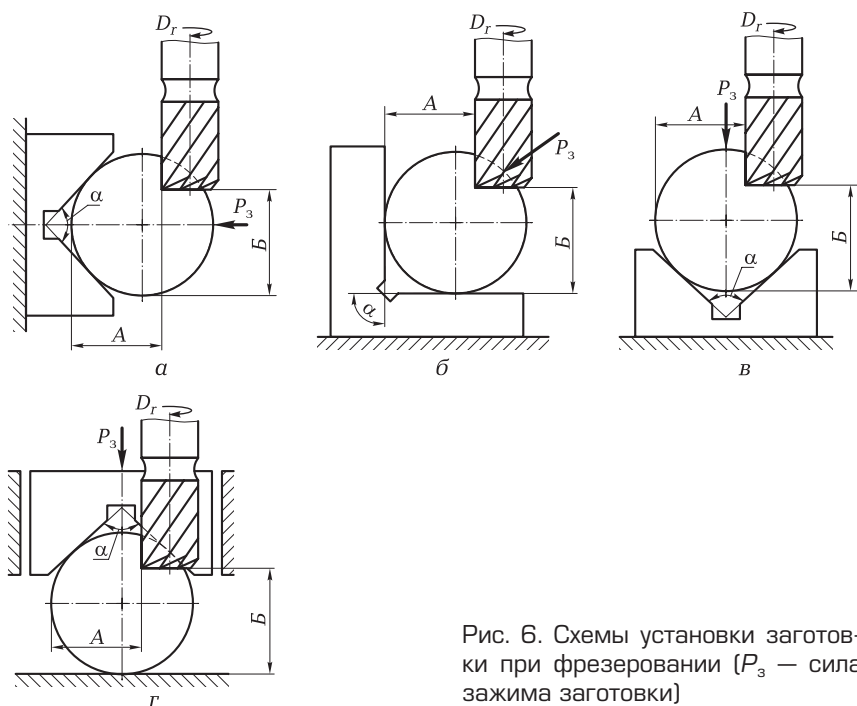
Схемы установки заготовки при фрезеровании [P_3 — сила зажима заготовки]
